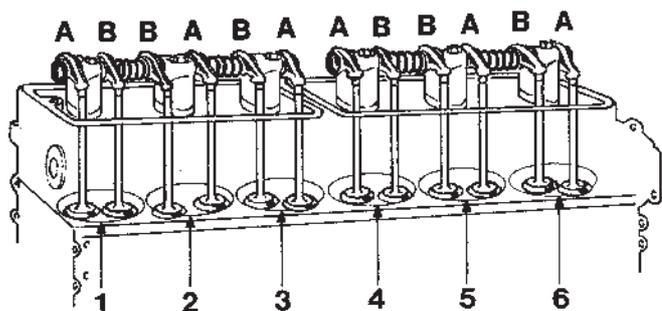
Emplacement des soupapes et numérotage des cylindres
